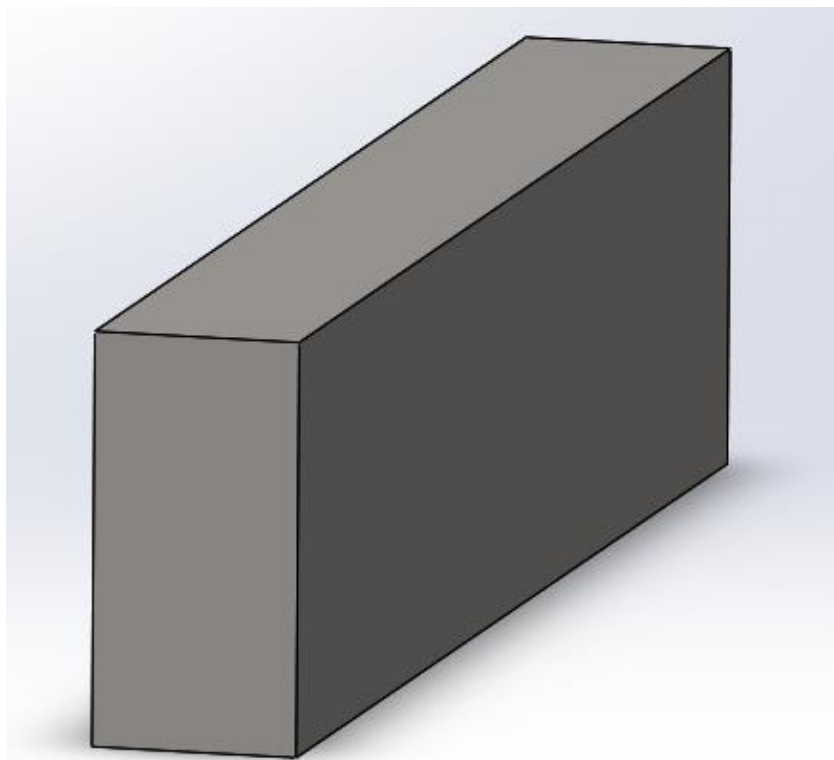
Vista isométrica do Macho projetado. Fonte: AUTOR.
